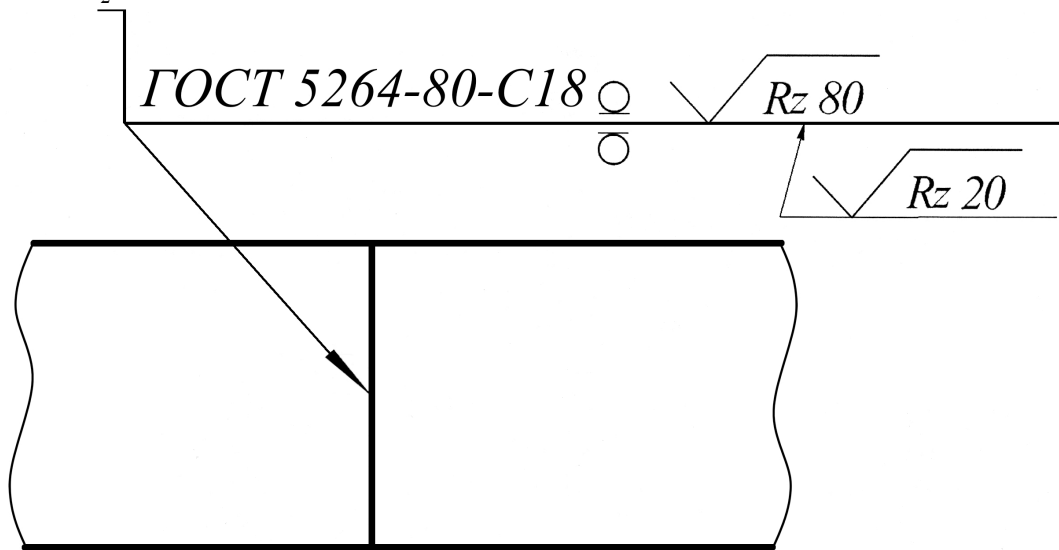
Условное обозначение сварного шва
